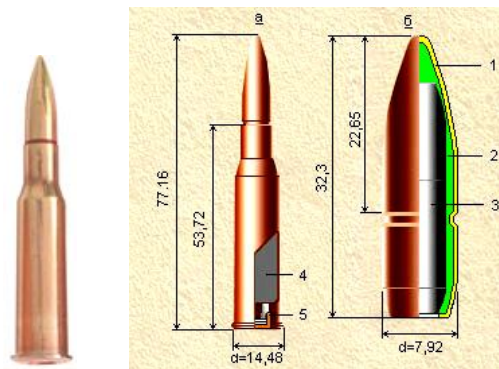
7,62-мм винтовочный патрон с пулей со стальным сердечником, а – патрон, б – пуля: 1 – оболочка; 2 – рубашка; 3 – сердечник стальной; 4 – метательный заряд; 5 – капсюль-воспламенитель
